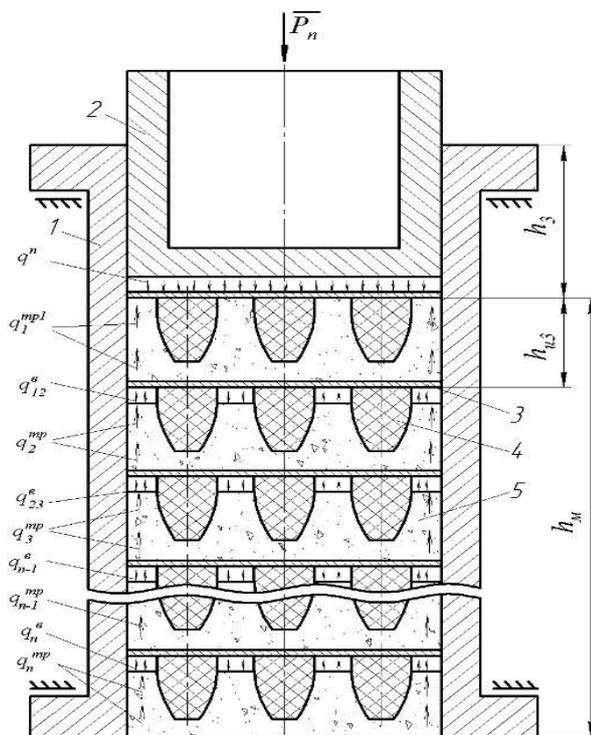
Расчетная схема процесса экструзивного формирования изделий с несквозными пустотными отверстиями
